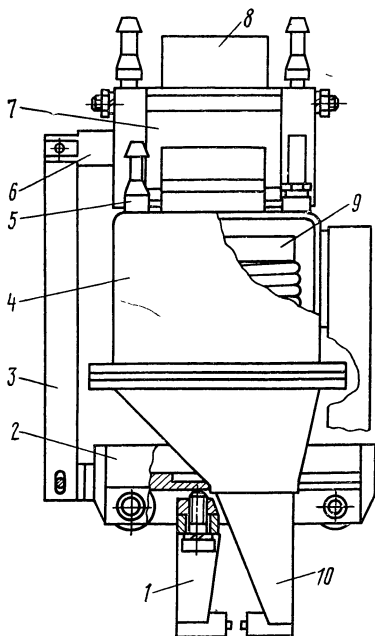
Конструкция сварочной головки клещей КТУ-1,5
